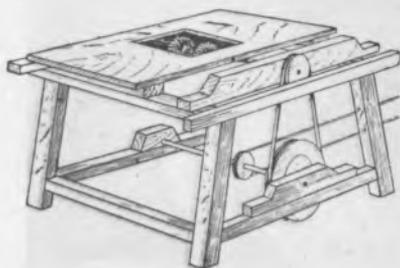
Чертеж станка для изготовления сапожных шпилек
